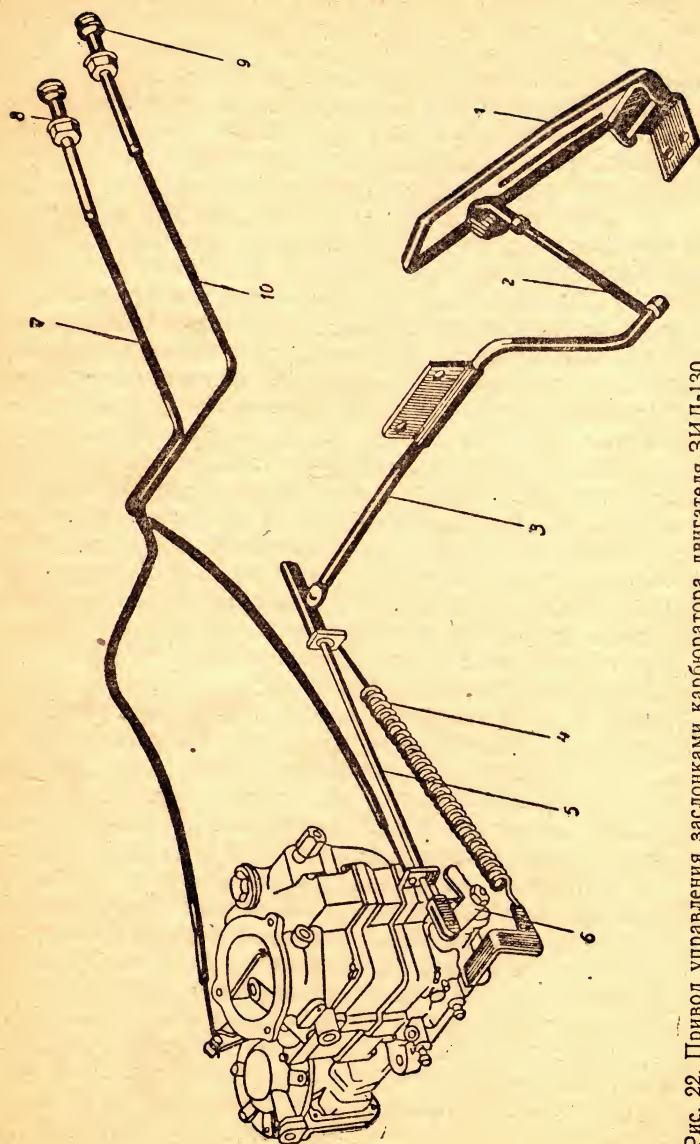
Привод управления заслонками карбюратора двигателя ЗИЛ-130
